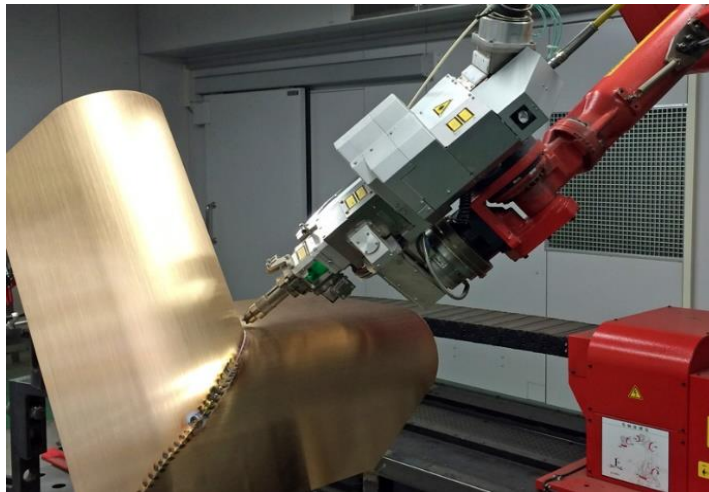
Robotizované svařování pod tavidlem (SAW) [16]
